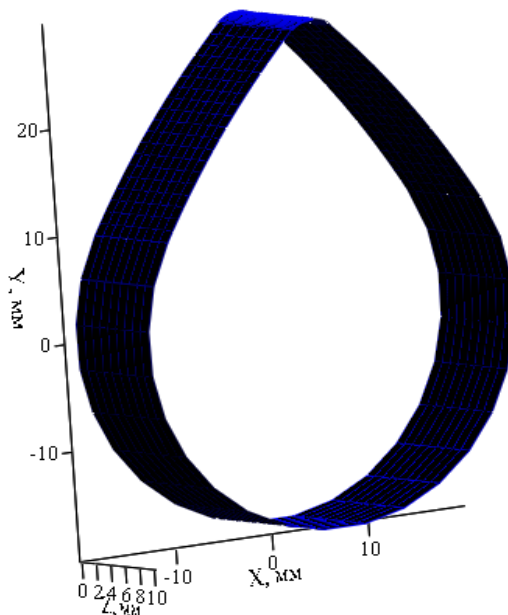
3D-модель поверхні кулачка розподільного вала
